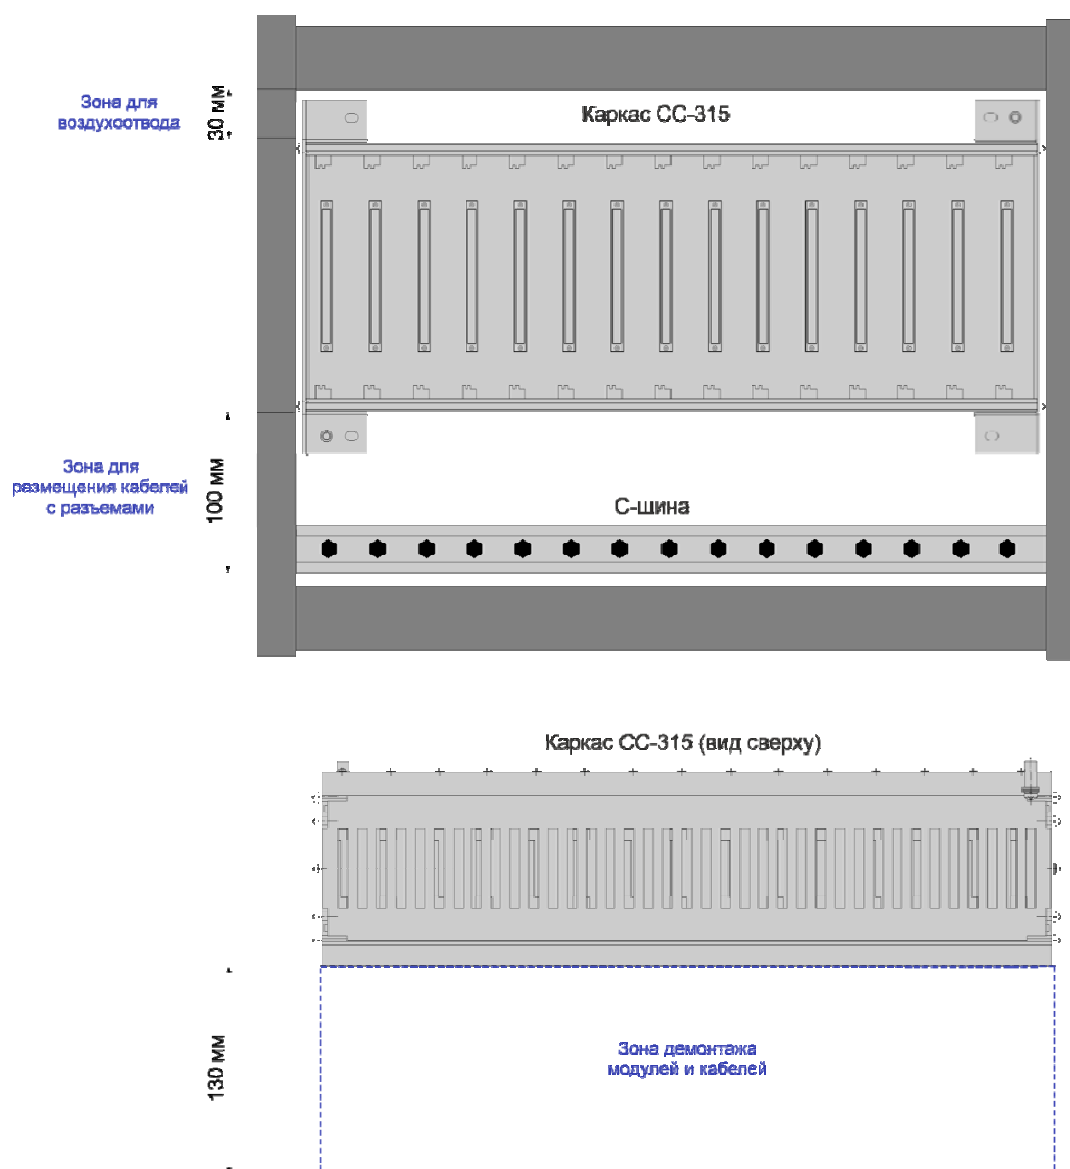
Монтаж крейта на базе каркаса CC-315 на монтажную панель шкафа (вид спереди и вид сверху)
